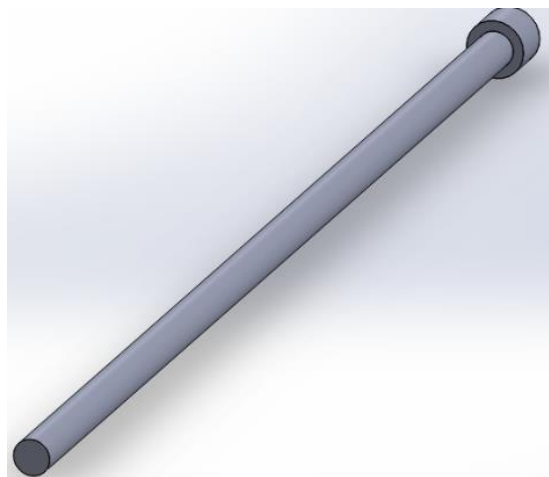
y 79: diseño y dimensiones de perno guía del pistón.
